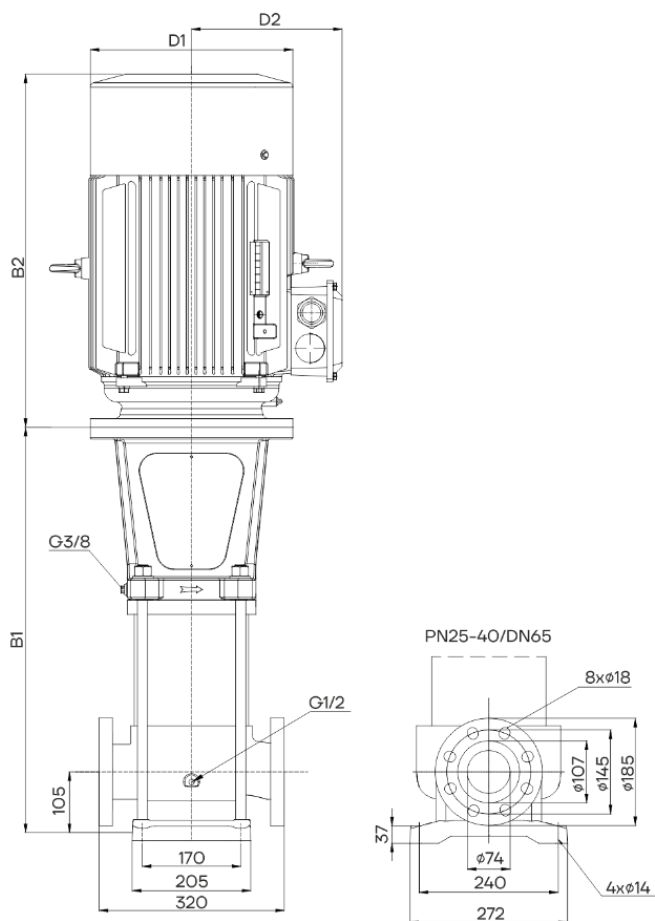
Д Габаритно-присоединительные размеры VMB(F)-H 32
